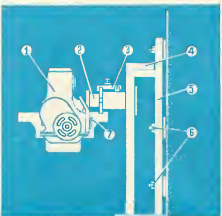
Стенд для разборки и сборки коробки передач автомобилей ЗИЛ и ГАЗ: 1 — коробка передач; 2 — поворотный стол; 3 — стойка (труба диаметром 100 мм); 4 — крючки для крепления стенда к стене (шаглер № 12); 5 — полка для инструментов; 6 — шарнир; 7 — откидная площадка; 8 — болты для крепления коробки передач; 9 — болты для крепления стенда к стене.
